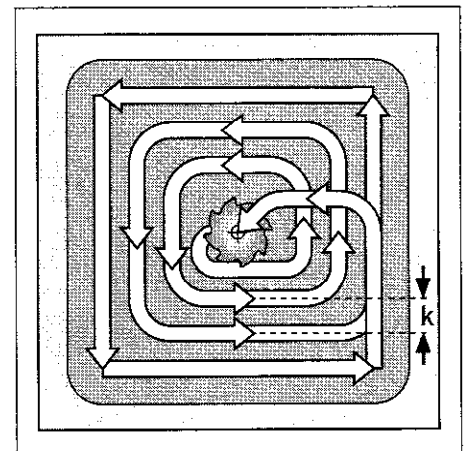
Werkzeug-Bahn beim Ausräumen
